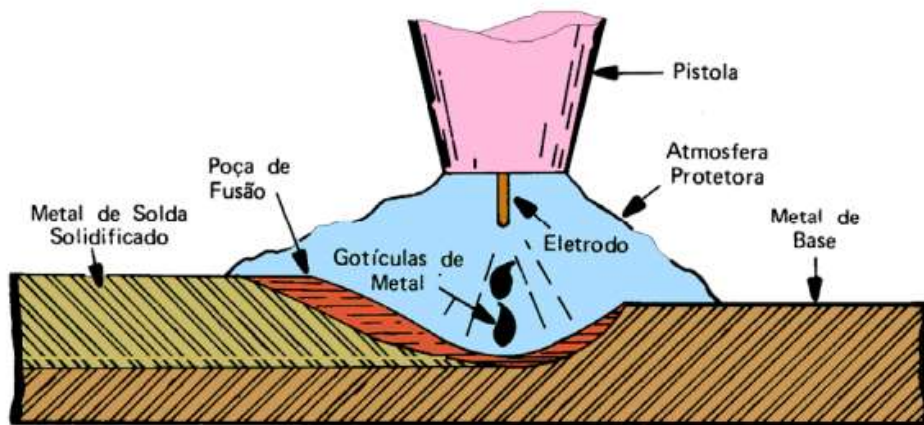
Processo de soldagem MIG/MAG⁽²⁸⁾.
